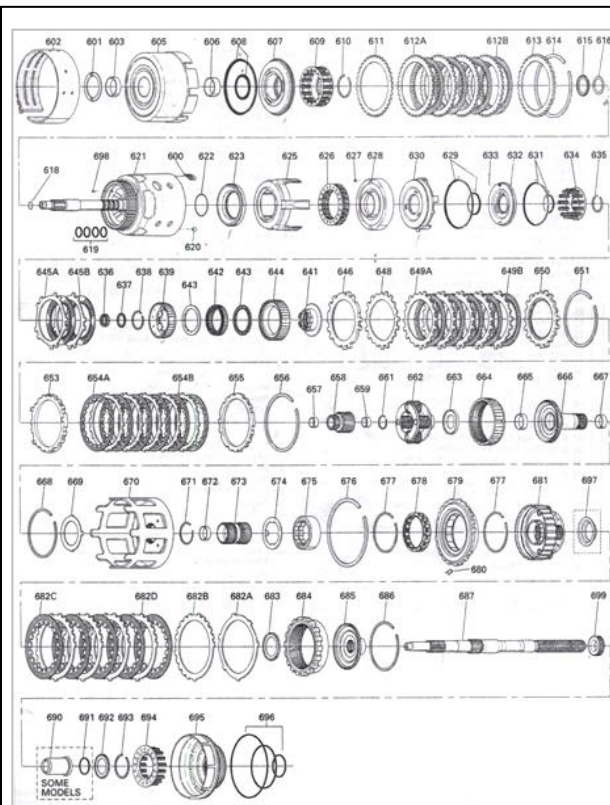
Despiece caja THM350 4L60-E parte interna
